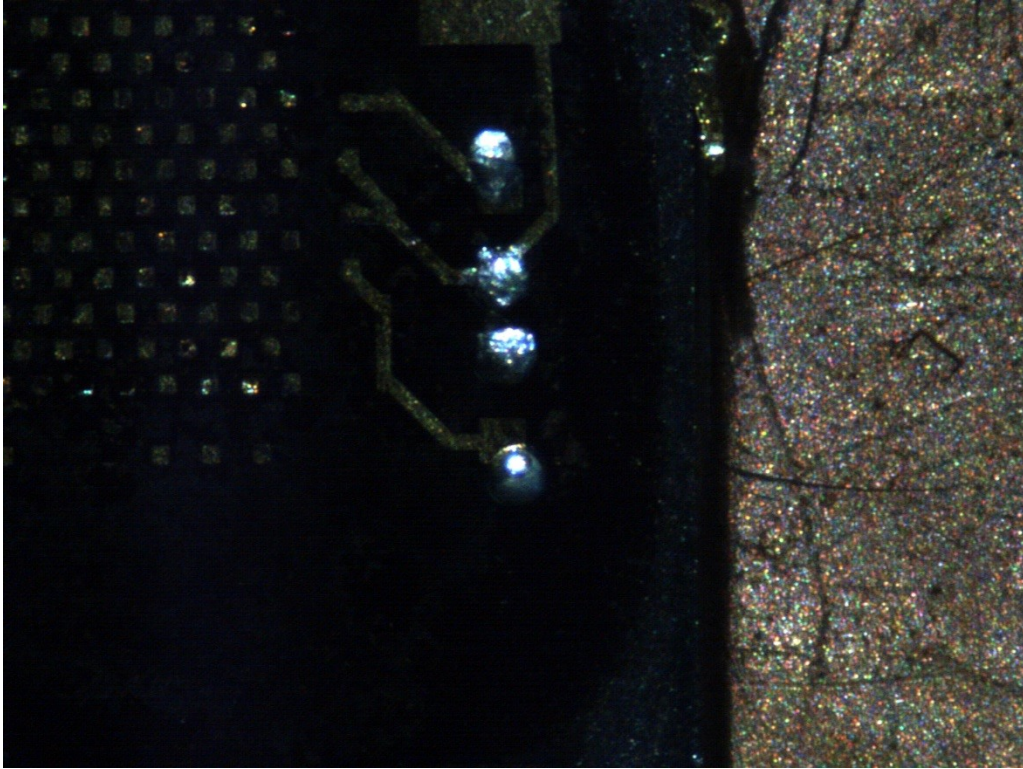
Billes de soudure après le *reflow* pour le test de soudure
